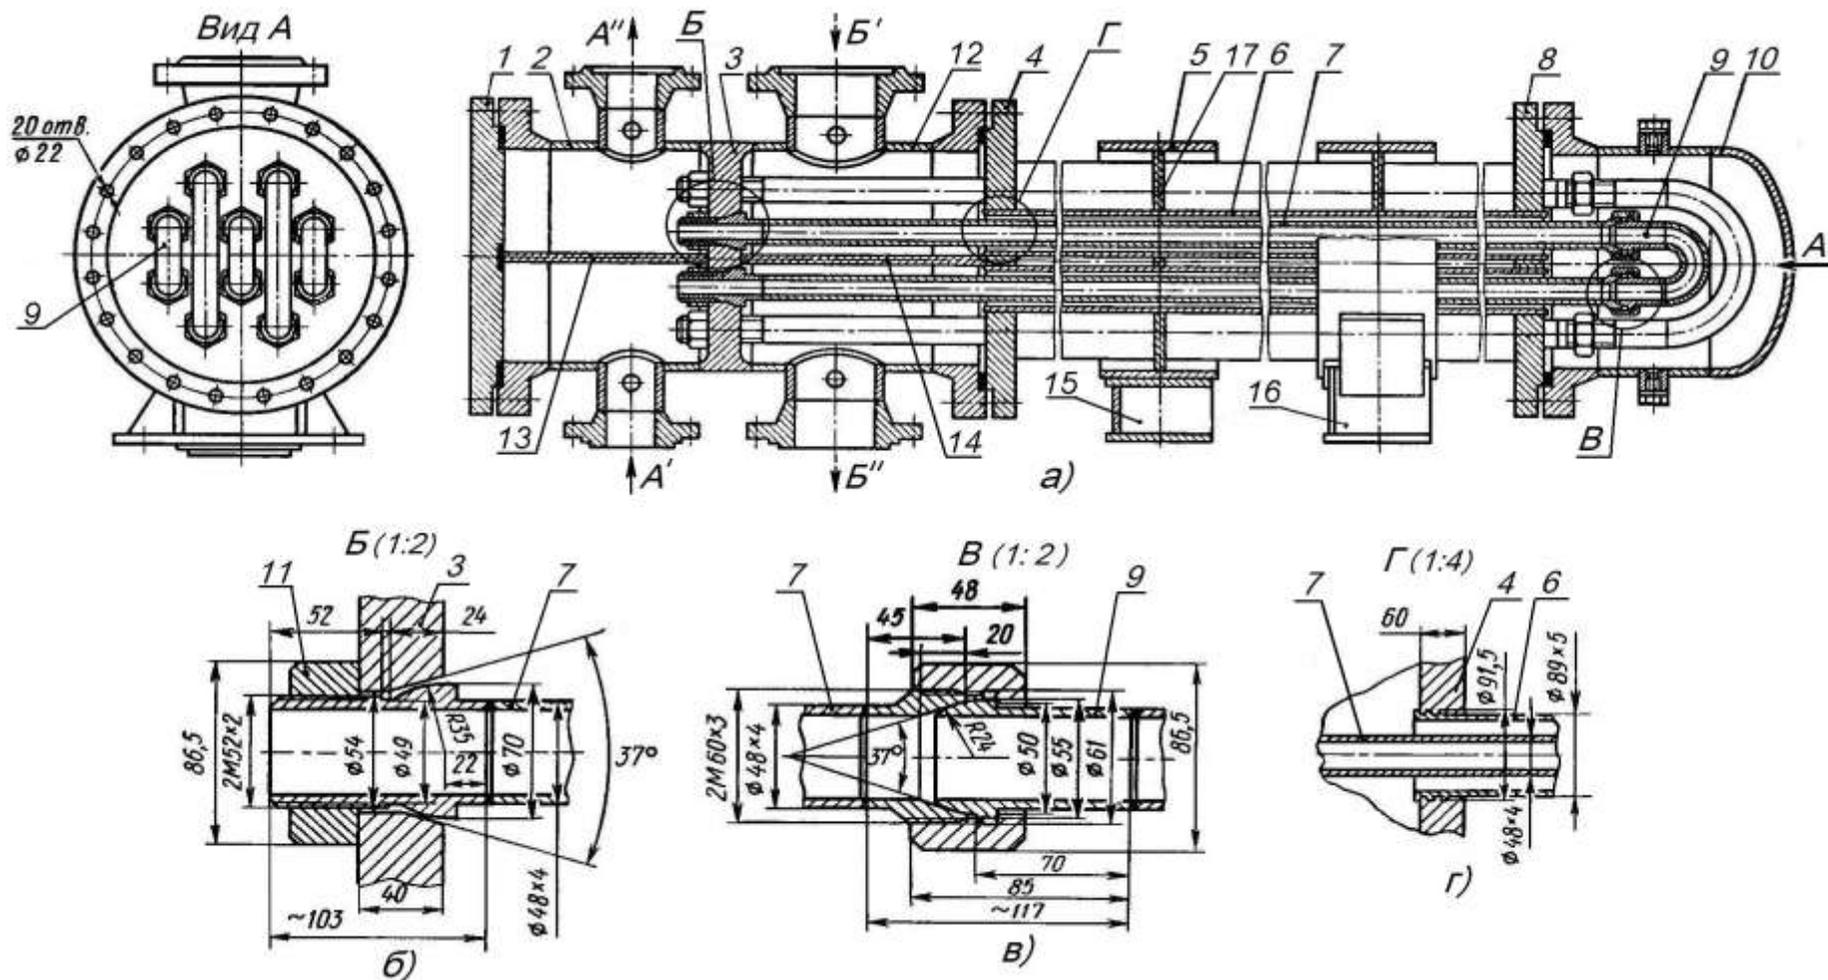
Двухпоточный разборный теплообменник типа «труба в трубе» нежесткой конструкции: а) – общий вид; б) – схема крепления передней трубной решетки 3 с внутренней трубой 7 с помощью гайки 11 с метрической резьбой; в) – схема соединения внутренней трубы 7 с двойником (отводом) 9 внутри крышки 10; г) – узел соединения наружной трубы 6 с средней трубной решеткой 4 методом вальцовки
